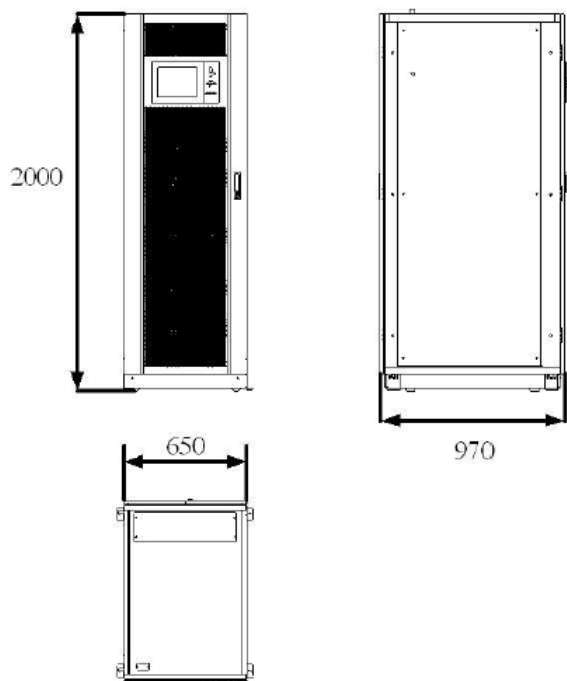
Размер для щитка 250-300КВА (Единицы: мм)
